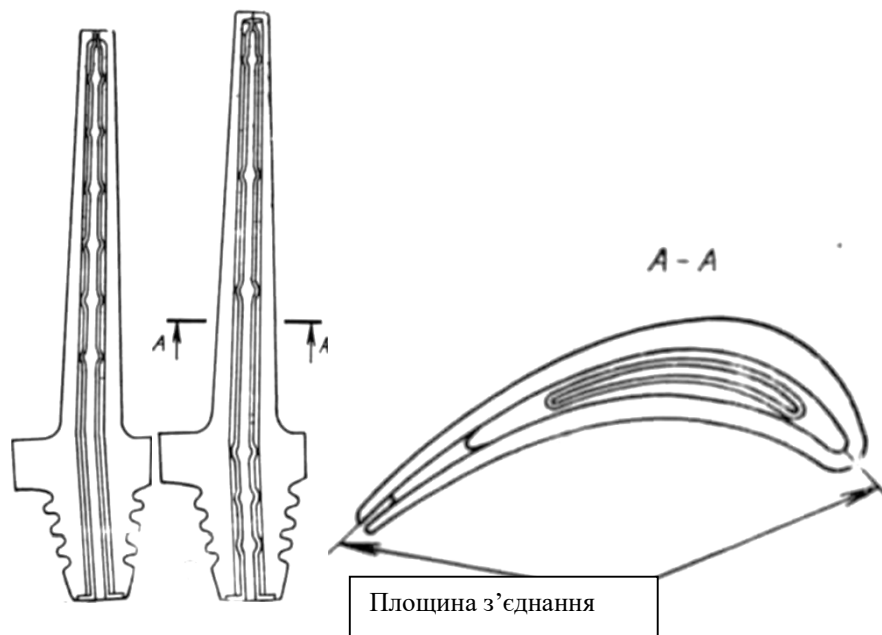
Розташування дефлектора всередині лопатки, звареної з двох частин.
